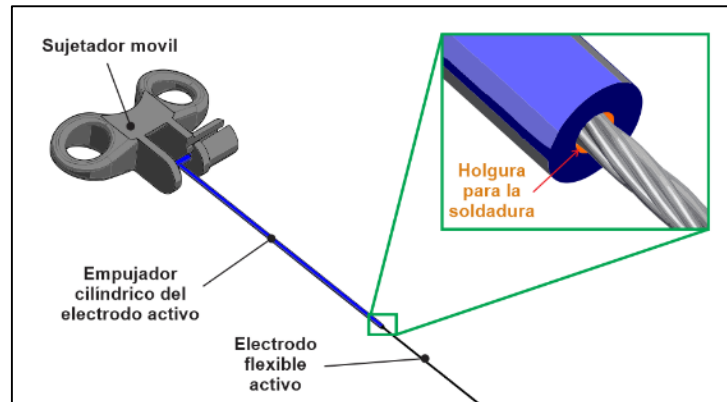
Esquema del conjunto sujetador móvil-cilindro guía y el lugar de la soldadura con el cable
